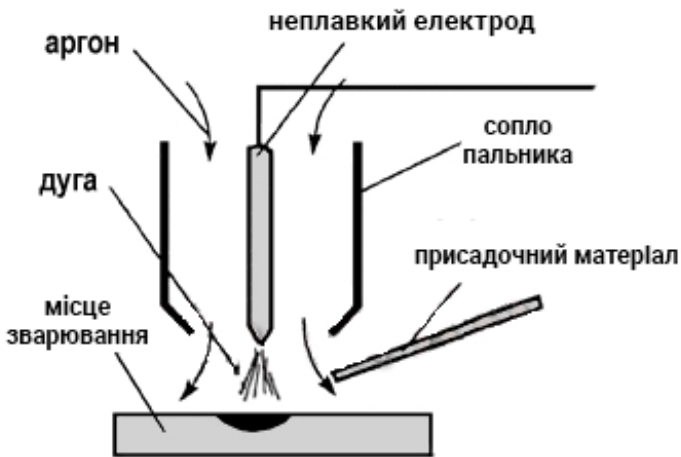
Розташування пальника і присадного матеріалу під час аргонодугового зварювання («TIG»).
